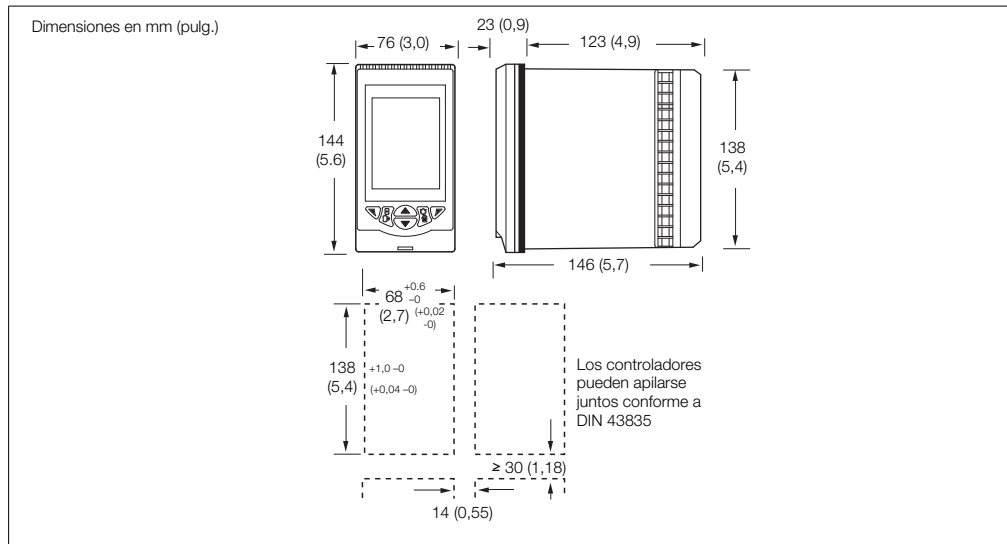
Dimensiones del ControlMaster CM10 y CM30
